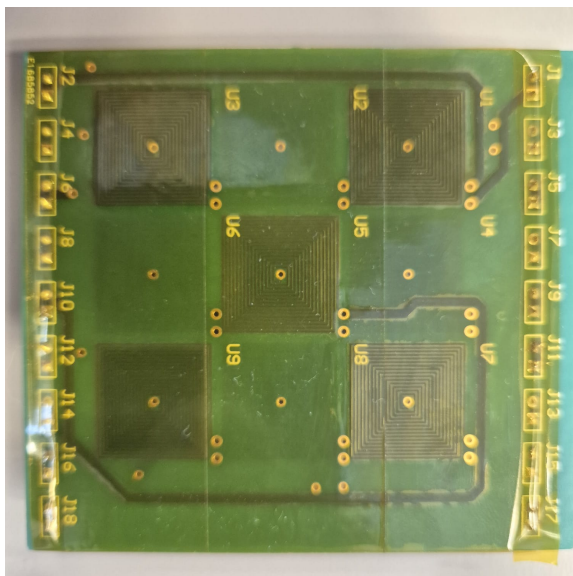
Recto de la carte des bobines complète et assemblée
